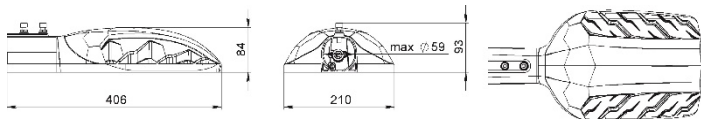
Общий вид светильника Street 9M с консольным креплением.
